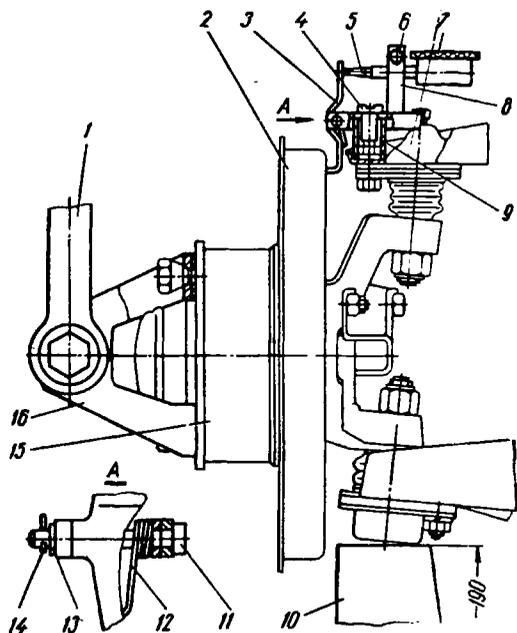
Замер зазора в верхнем шаровом шарнире приспособлением 02.8701.9500 (тормоз условно не показан): 1 - динамометрический ключ; 2 - защитный кожух тормоза; 3 - рычажок; 4 - винт; 5 - удлинитель индикатора; 6 - болт; 7 - индикатор; 8 - основание; 9 - втулка; 10 - колодка; 11 - ось; 12 - пружина; 13 - шайба; 14 - шплинт; 15 - ступица колеса; 16 - кронштейн
